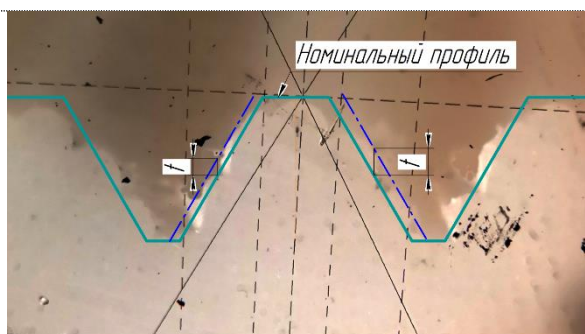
Профиль резьбы М8, сформированной в образце из PLA-пластика
